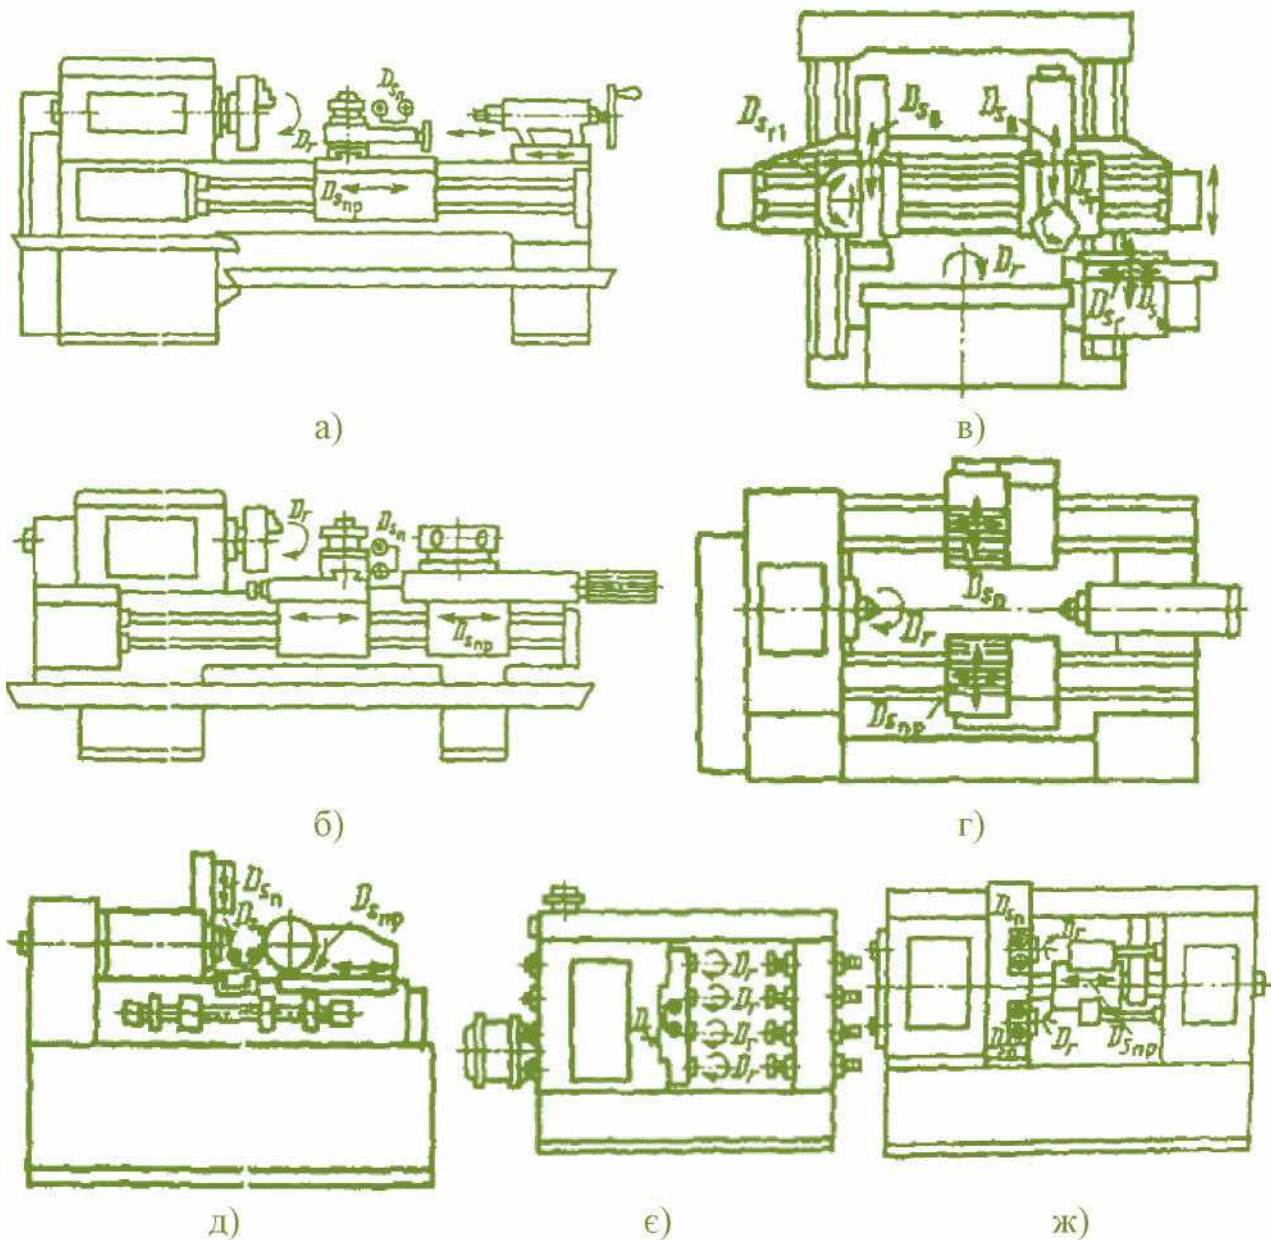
Загальні види верстатів токарної групи (стрілками без позначення вказані установочні рухи вузлів верстатів)
